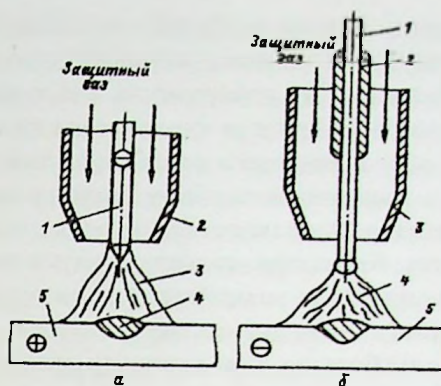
Схема процесса сварки в среде защитных газов:
